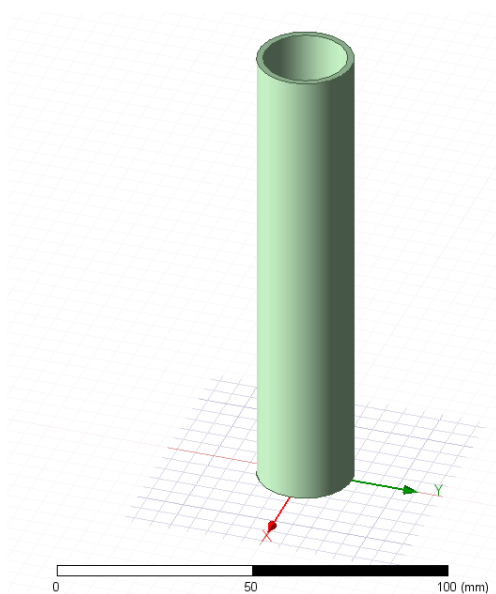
Вигляд зовнішньої сторони стержня
